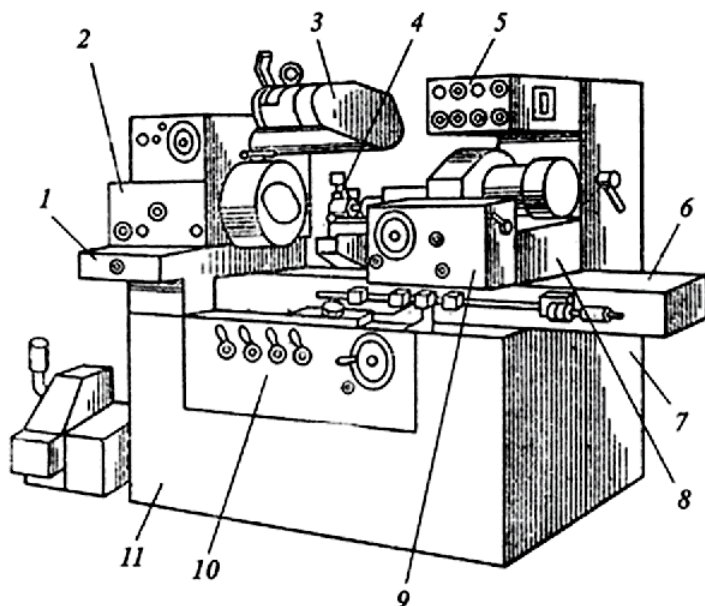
Внутришлифовальный станок мод. 3К227В
